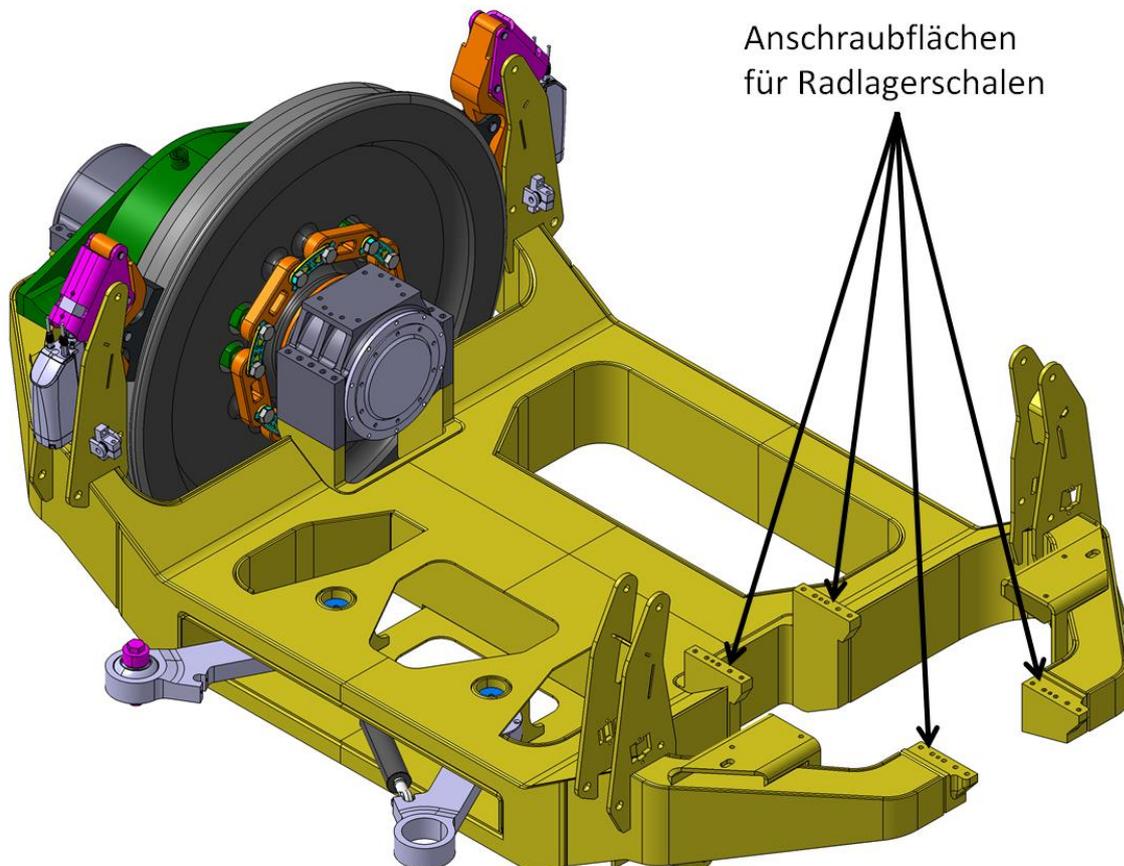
Detailansicht: Radträgerschweißbaugruppe mit einer der zwei Radbaugruppen
